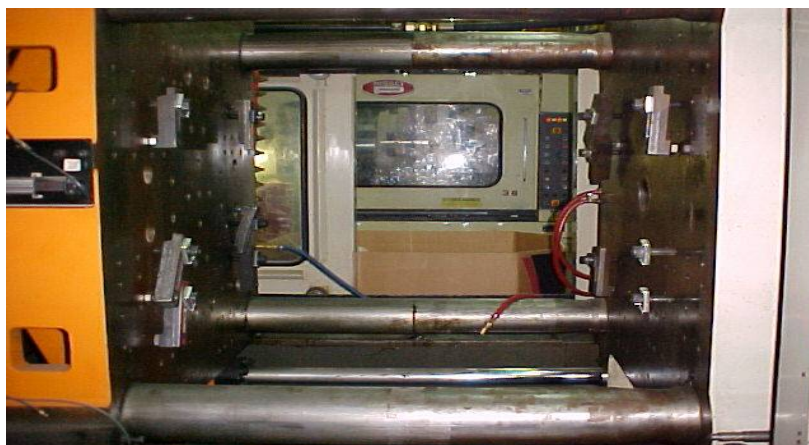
Platinas de maquina moldeadora cincinnati milacron.
